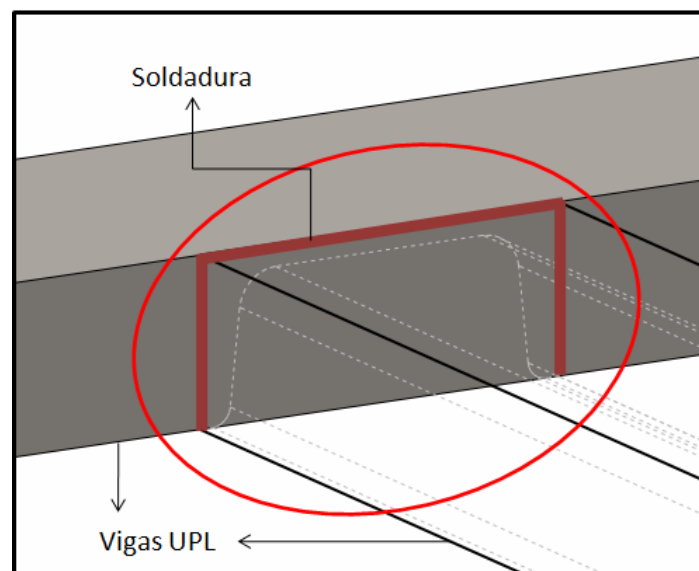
Viga UPL 80 sometida a soldadura [Fuente: propio].
